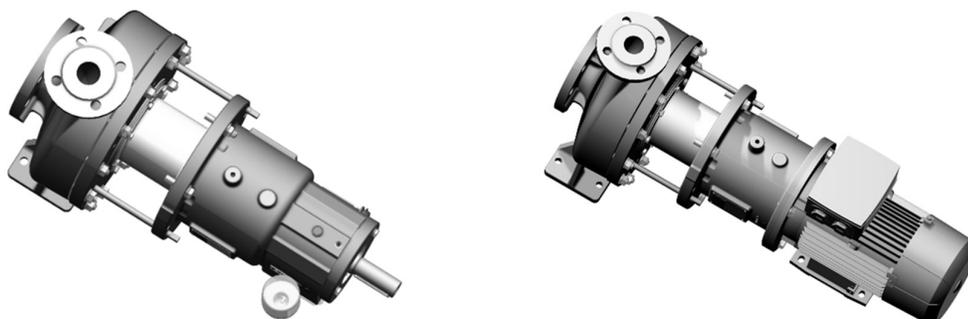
Montaje del extremo del motor y del extremo húmedo para CBMM (izquierda) y CBME (derecha)
